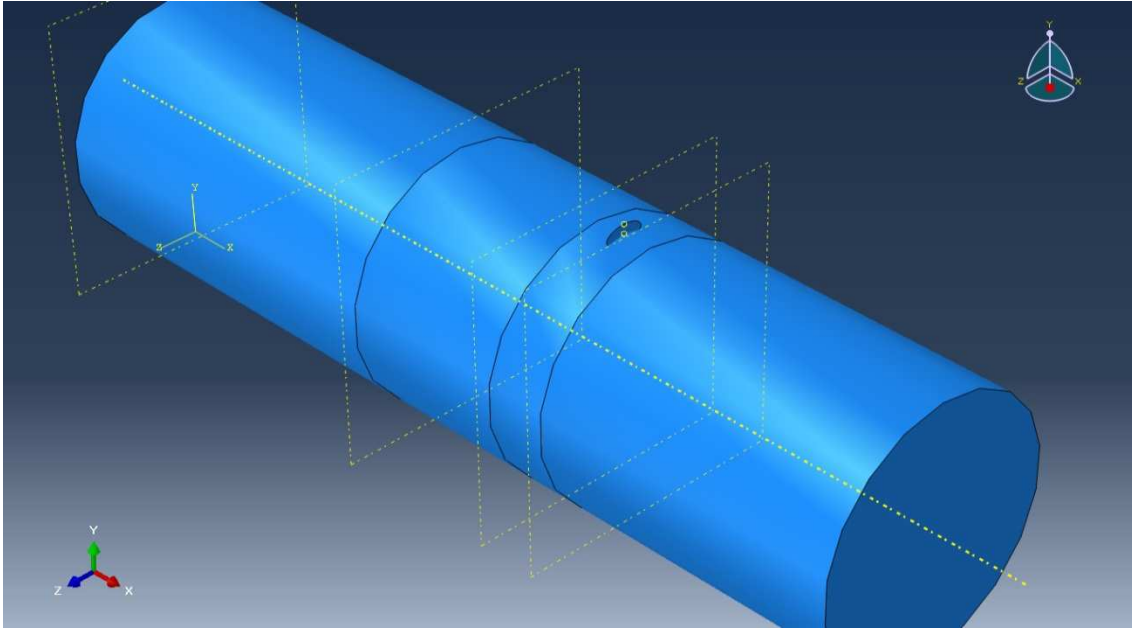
"Eje cilíndrico" con grieta posicionada
